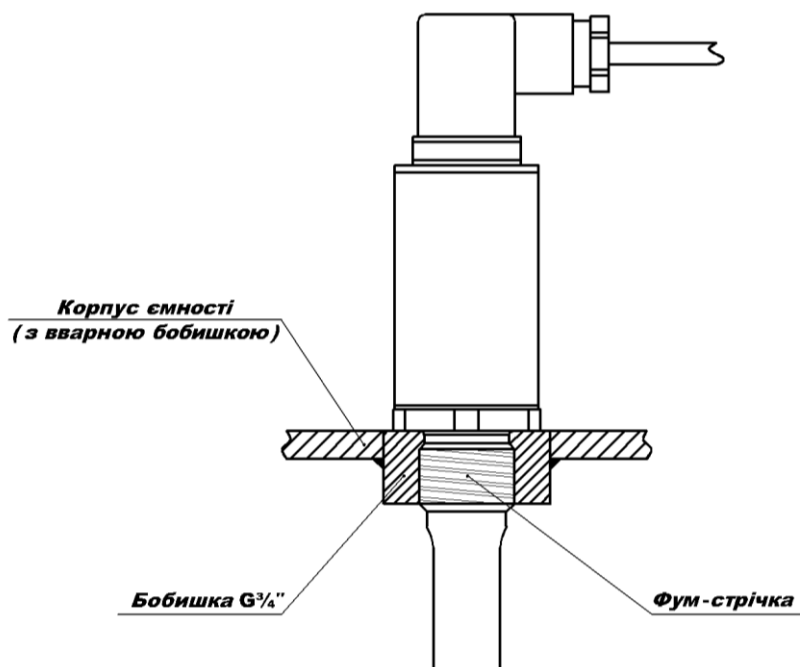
Установка Датчика на корпус ємності з ввареною бобишкою.
